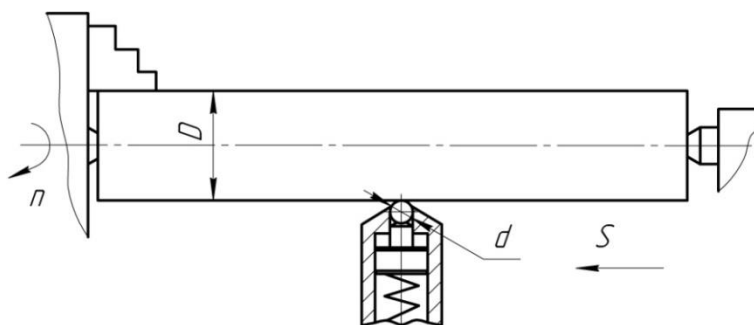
Схема обробки поверхні кульковим обкатником:
